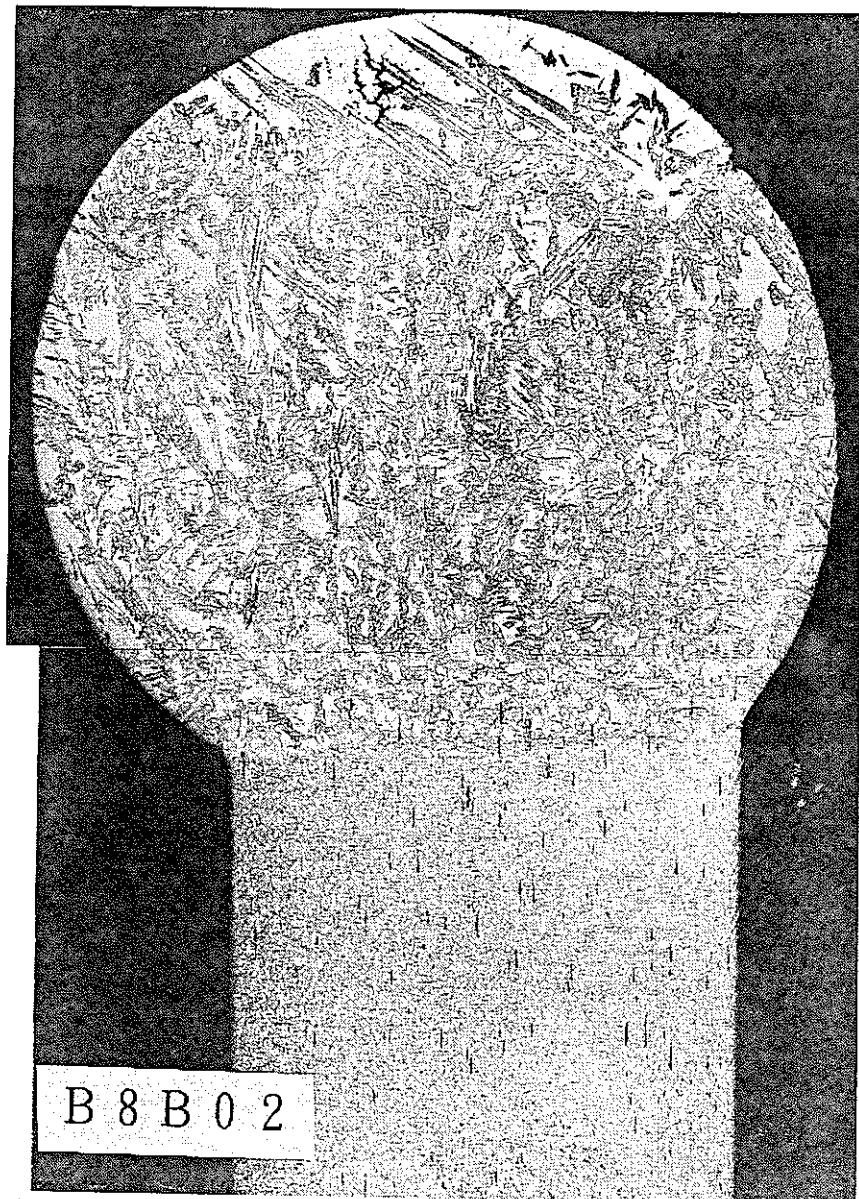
ワイヤ玉止溶接施行断面金相写真（下部）
